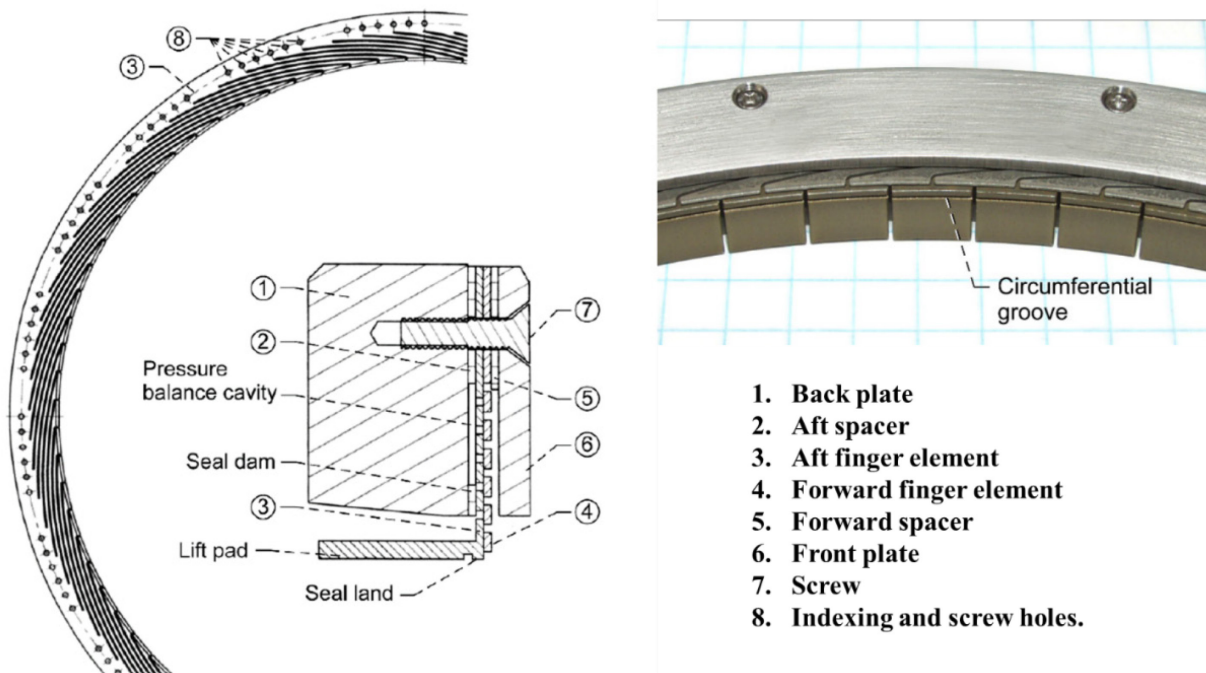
Géométrie et assemblage des finger seals sans contact [13]
